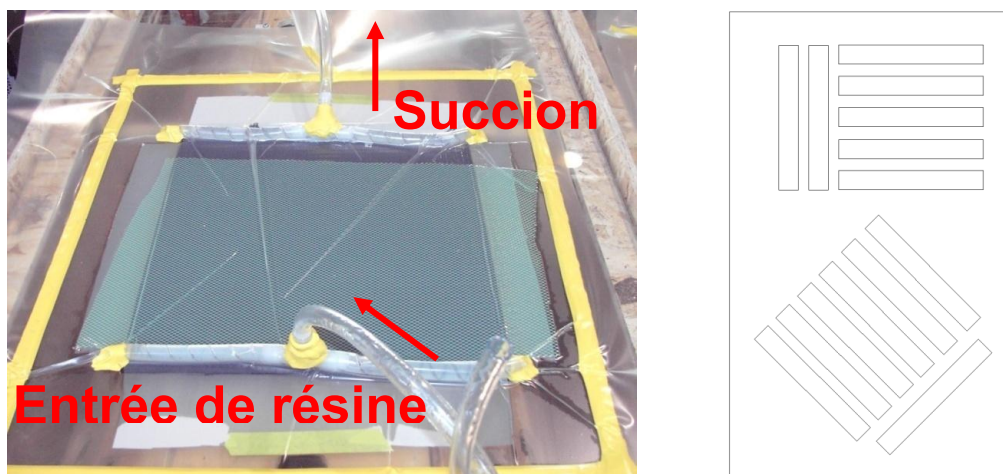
Montage pour la fabrication d'une plaque (gauche) et gabarit de découpe (droite)
